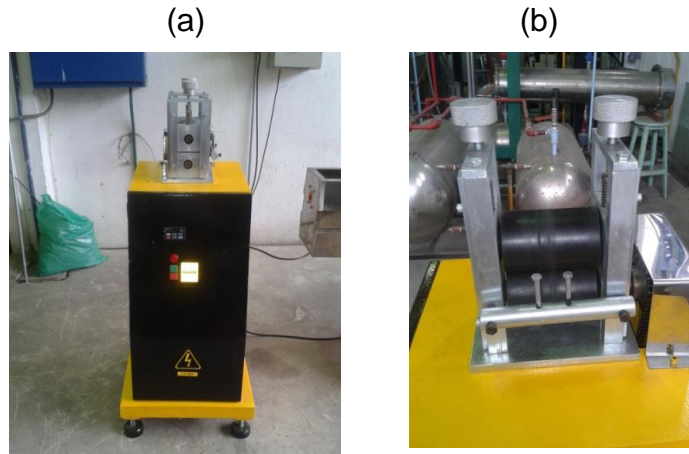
(a) Hilador. (b) Rodillos del hilador. Fuente: Autor
